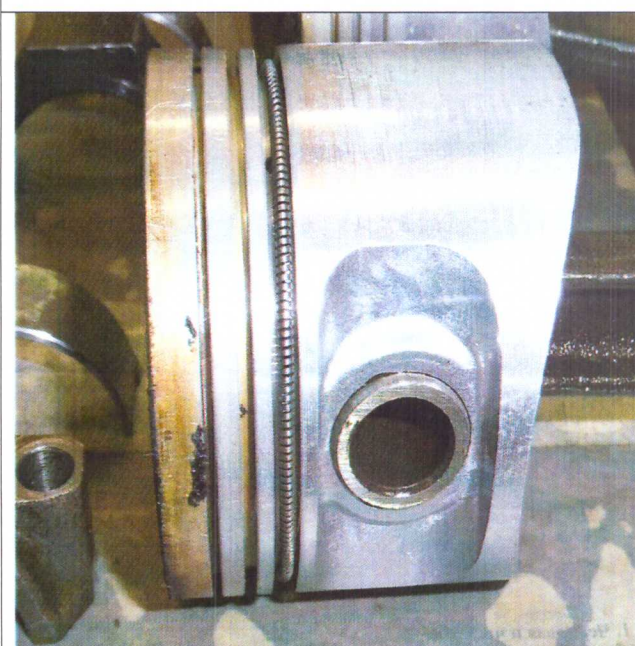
Внешний вид боковой поверхности поршня четвертого цилиндра по окончании длительных испытаний двигателя при работе на базовом масле Castrol EDGE
